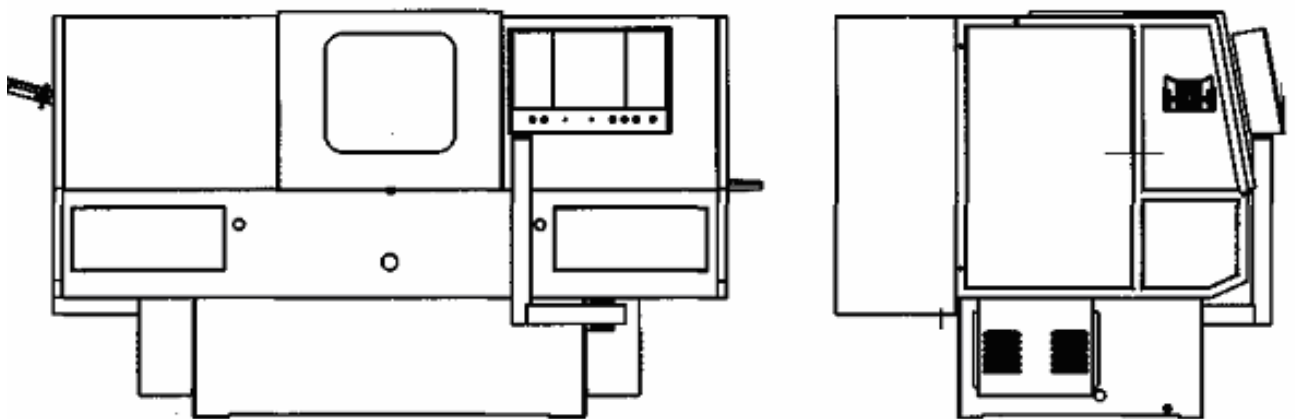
Загальний вигляд двошпindelного токарного верстата з ЧПК
